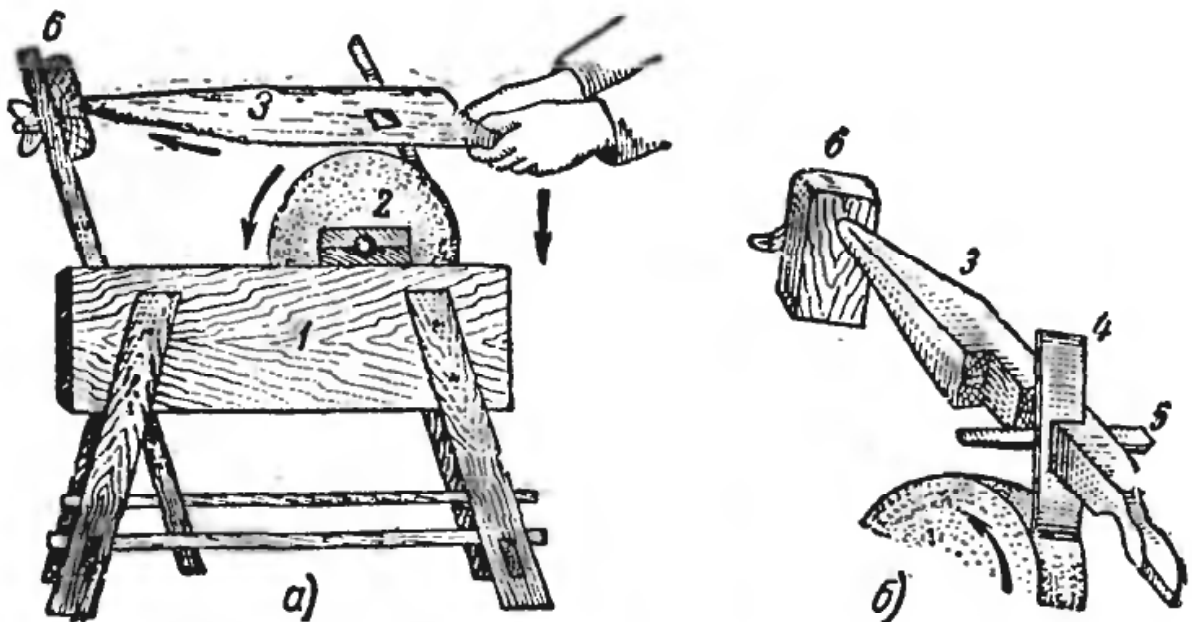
Точка на круглом точиле железки рубанка, зажатого в деревянный брусок: *a* — точило; *б* — установка зажимного бруска; *1* — корыто для точила с водой (вид сбоку); *2* — точильный камень; *3a* — брусок для зажима железки (вид сбоку); *3б* — вид бруска в разрезе; *4* — железка; *5* — зажимной клин; *6* — опорная планка для бруска с шарниром.
